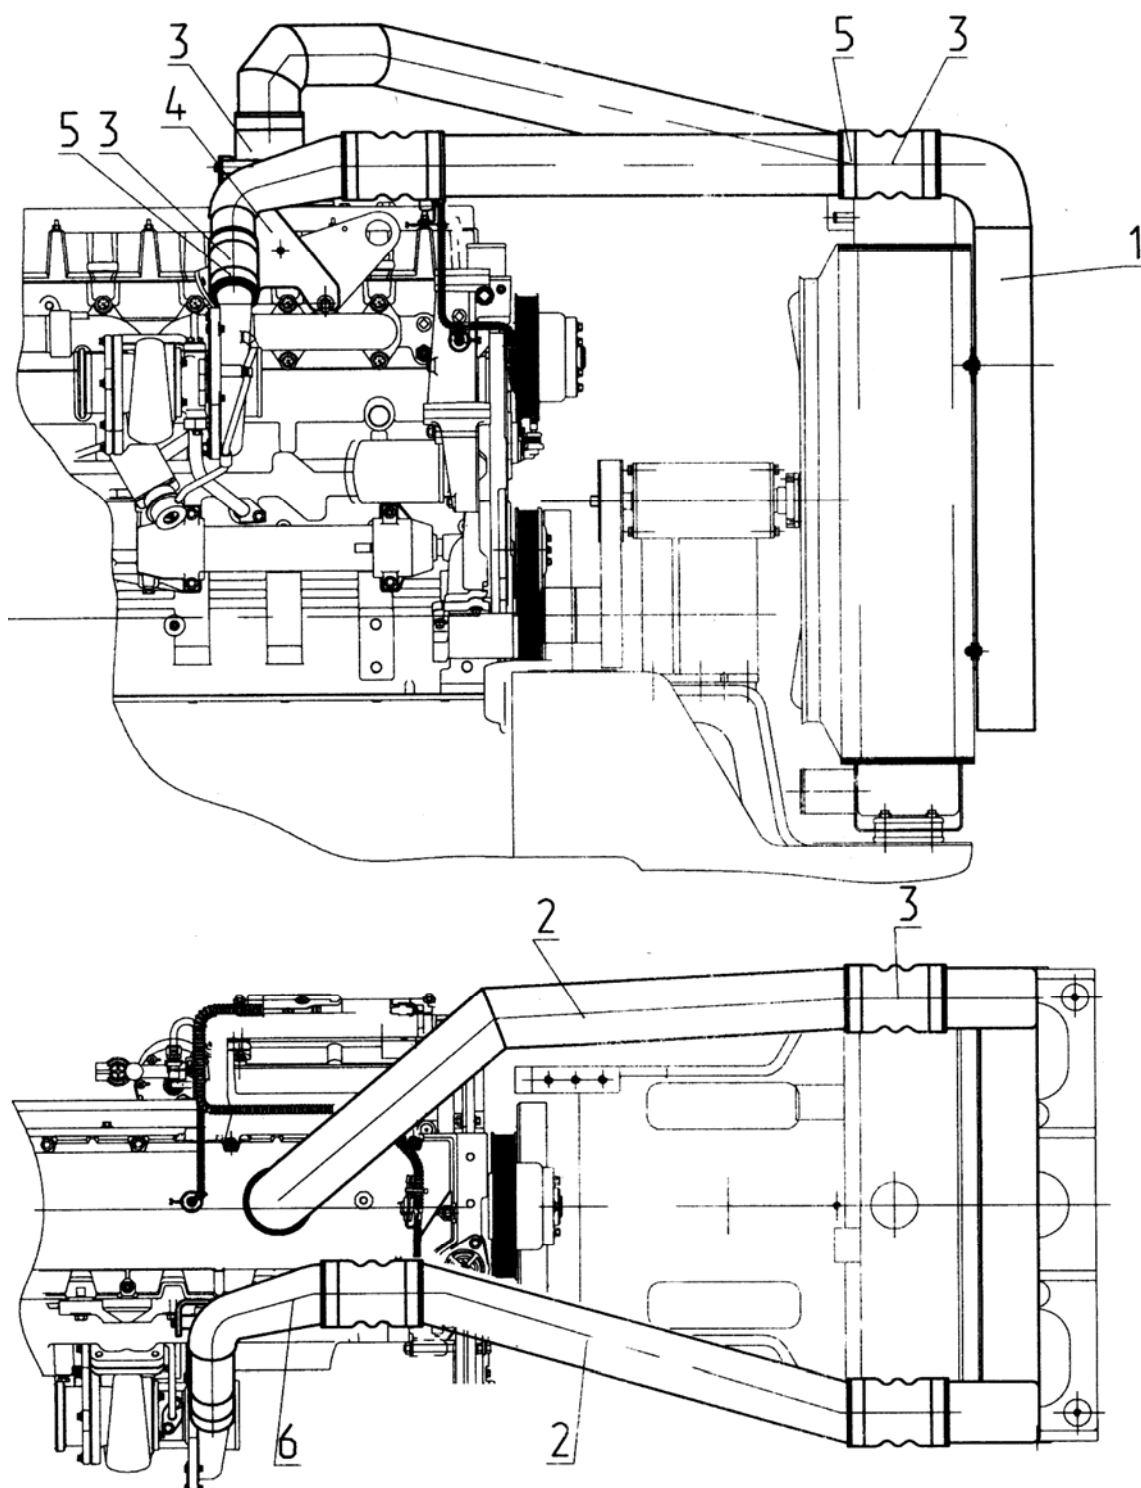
Установка охладителя наддувочного воздуха, двигателя DETROIT DIESEL.
